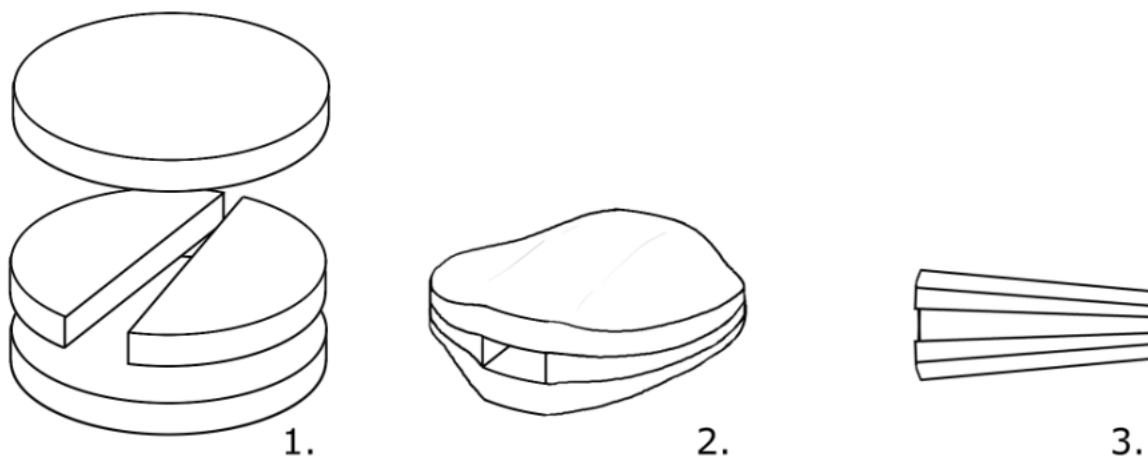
Procédé par empilement et soudage. Dessin F. Cognot.
